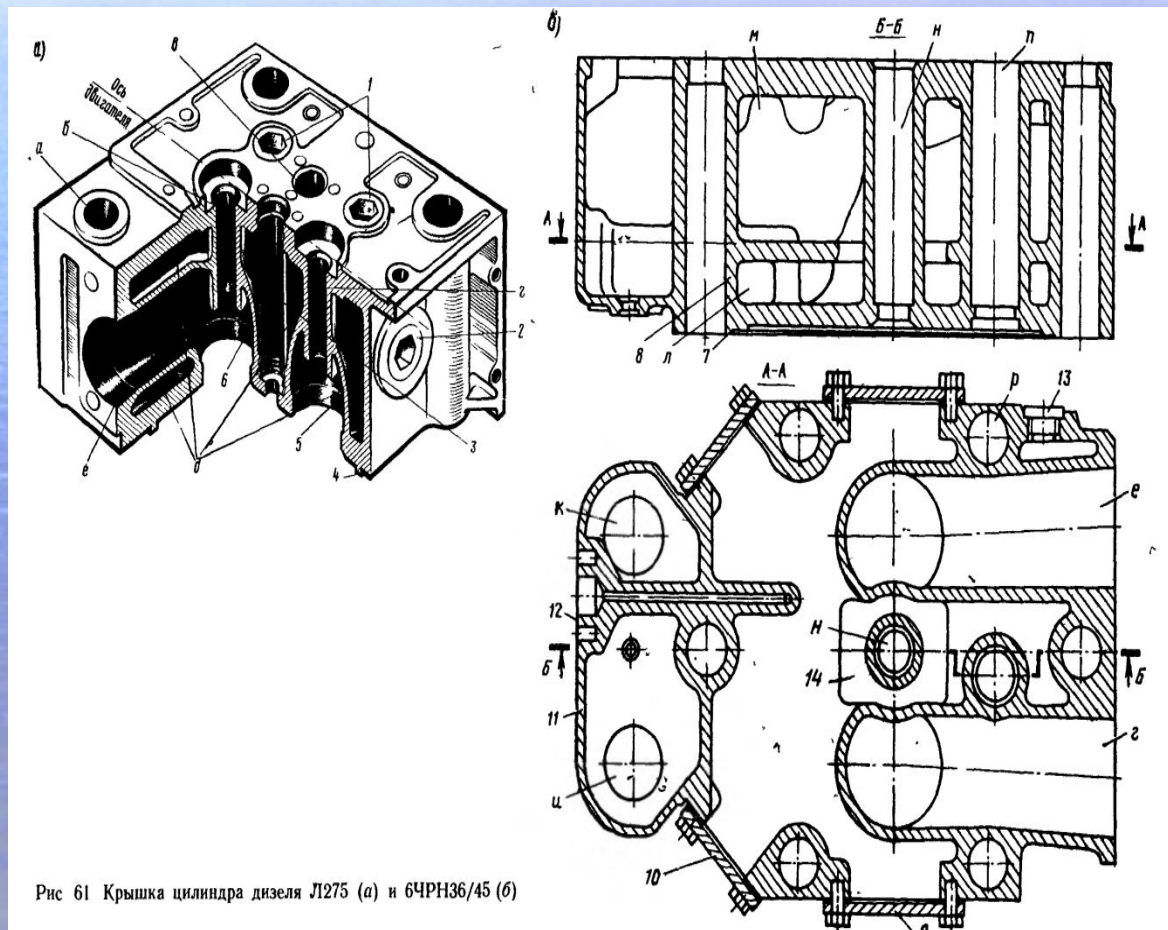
Крышка цилиндра дизеля J1275 (а) и 6ЧРН36/45 (б)
